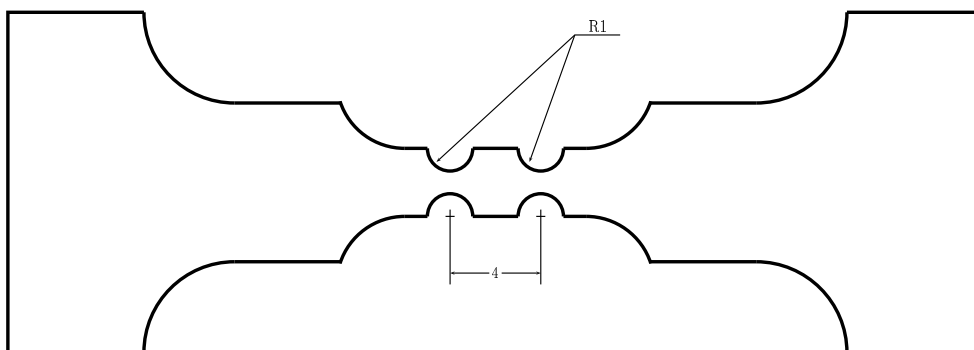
Schéma des éprouvettes à entaille double (cas de la Y6). Vue de face, épaisseur 2 mm.
